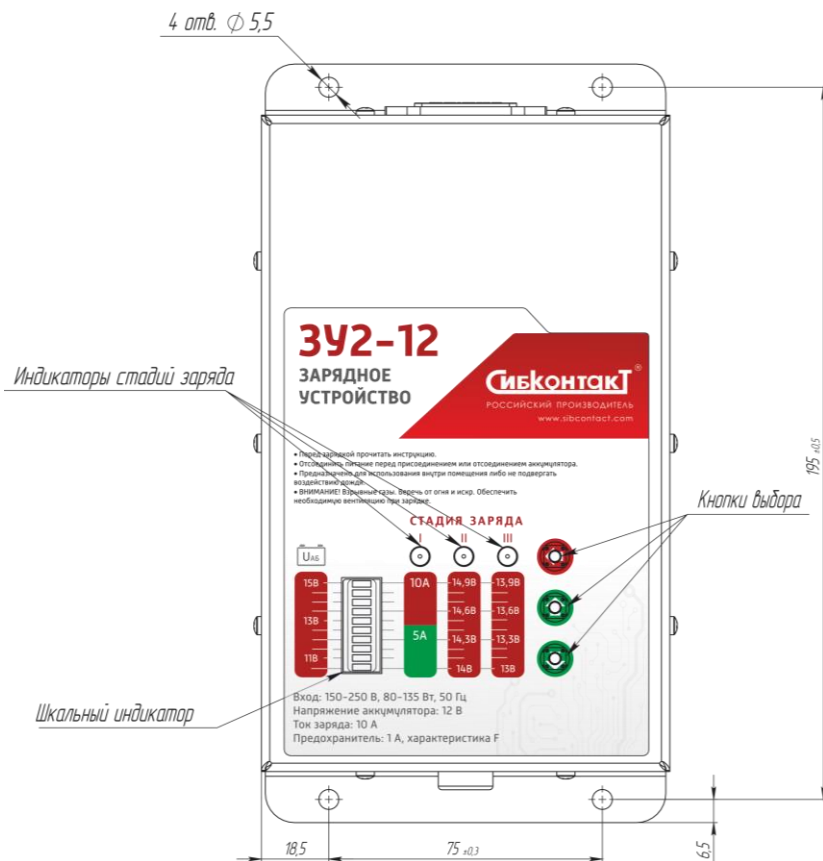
Внешний вид лицевой панели и установочные размеры зарядного устройства
